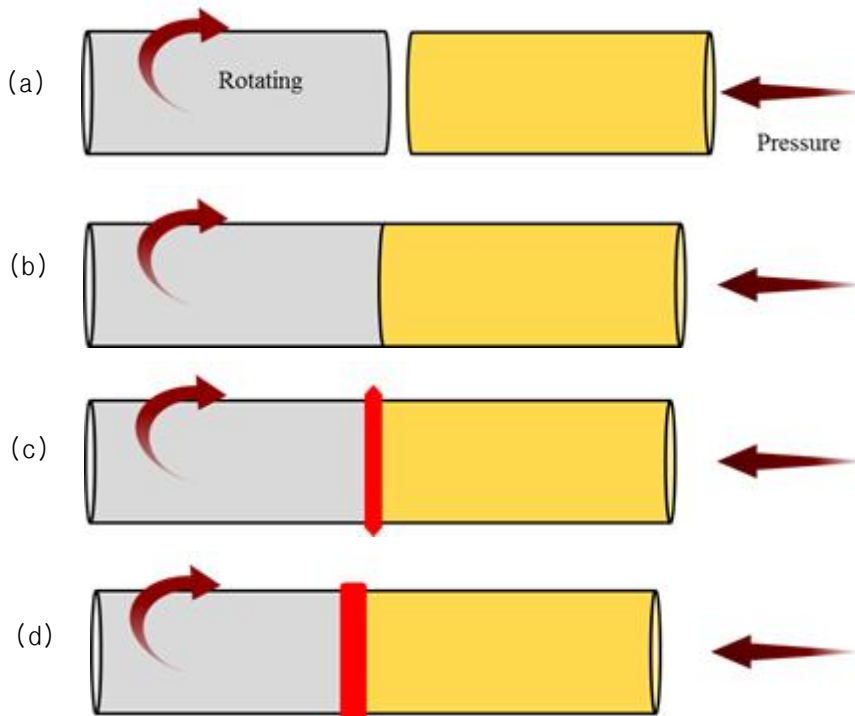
마찰접합기술의 기본 공정. (a) preparation, (b) material contact, (c) heat transfer와 (d) forge pressure/weld finish.
